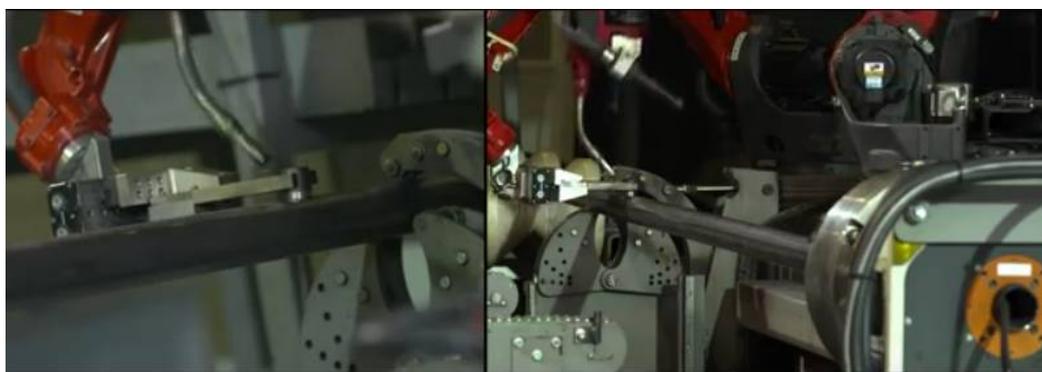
Célula de Soldadura de *sprinkler* em tubos para sistemas de incêndio
